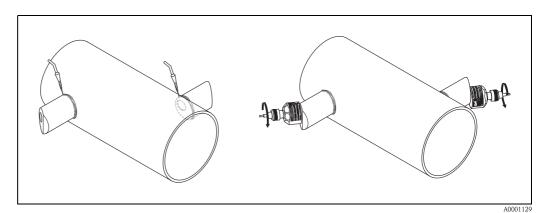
Montaggio dei sensori di misura, fasi 10 - 12
